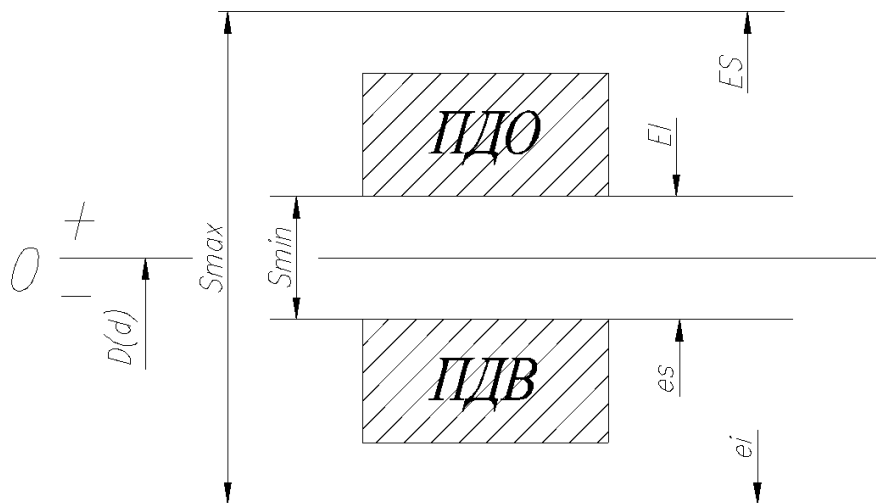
Схема розташування полів допусків з'єднання з зазором
